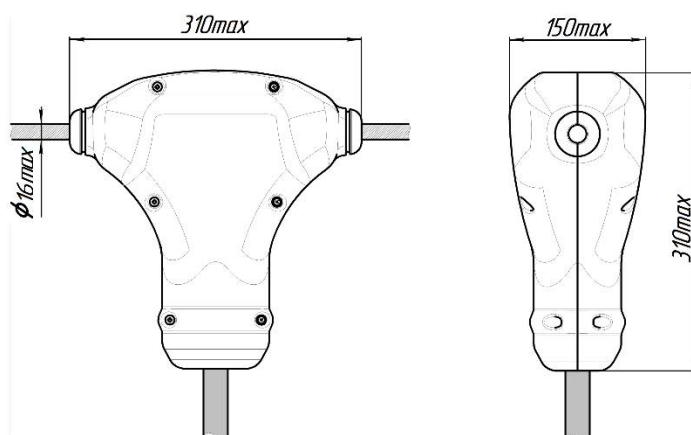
Габаритные и установочные размеры ДИЭ
